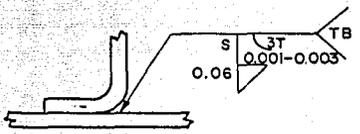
APLICACION DE SIMBOLOS DE SOLDADURA CON LATON
